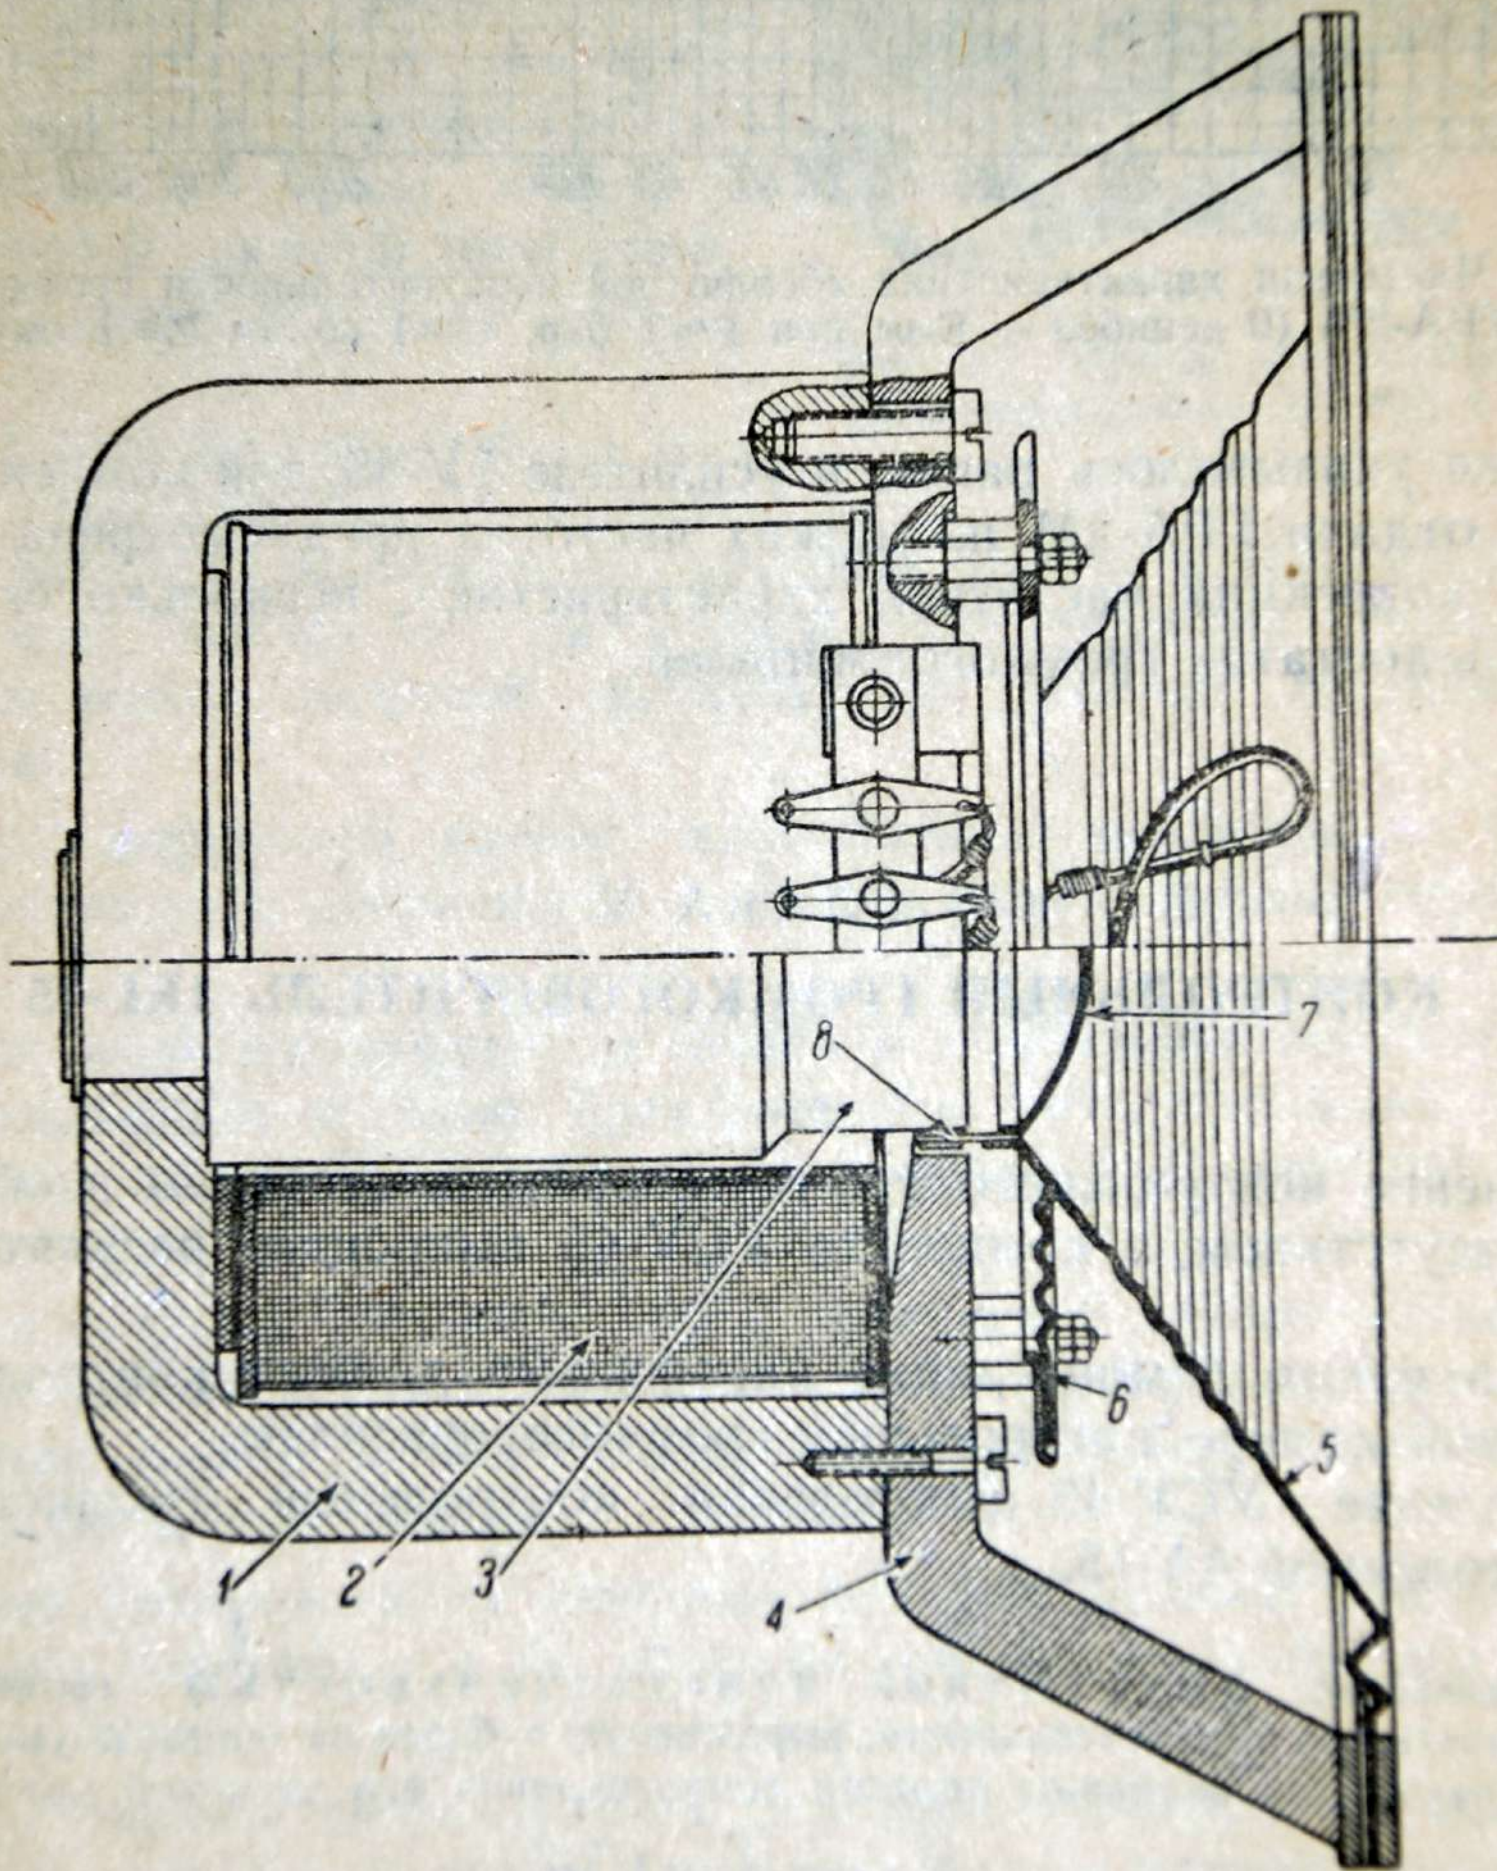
Головка 1А-10 (эскизный чертеж конструкции)
